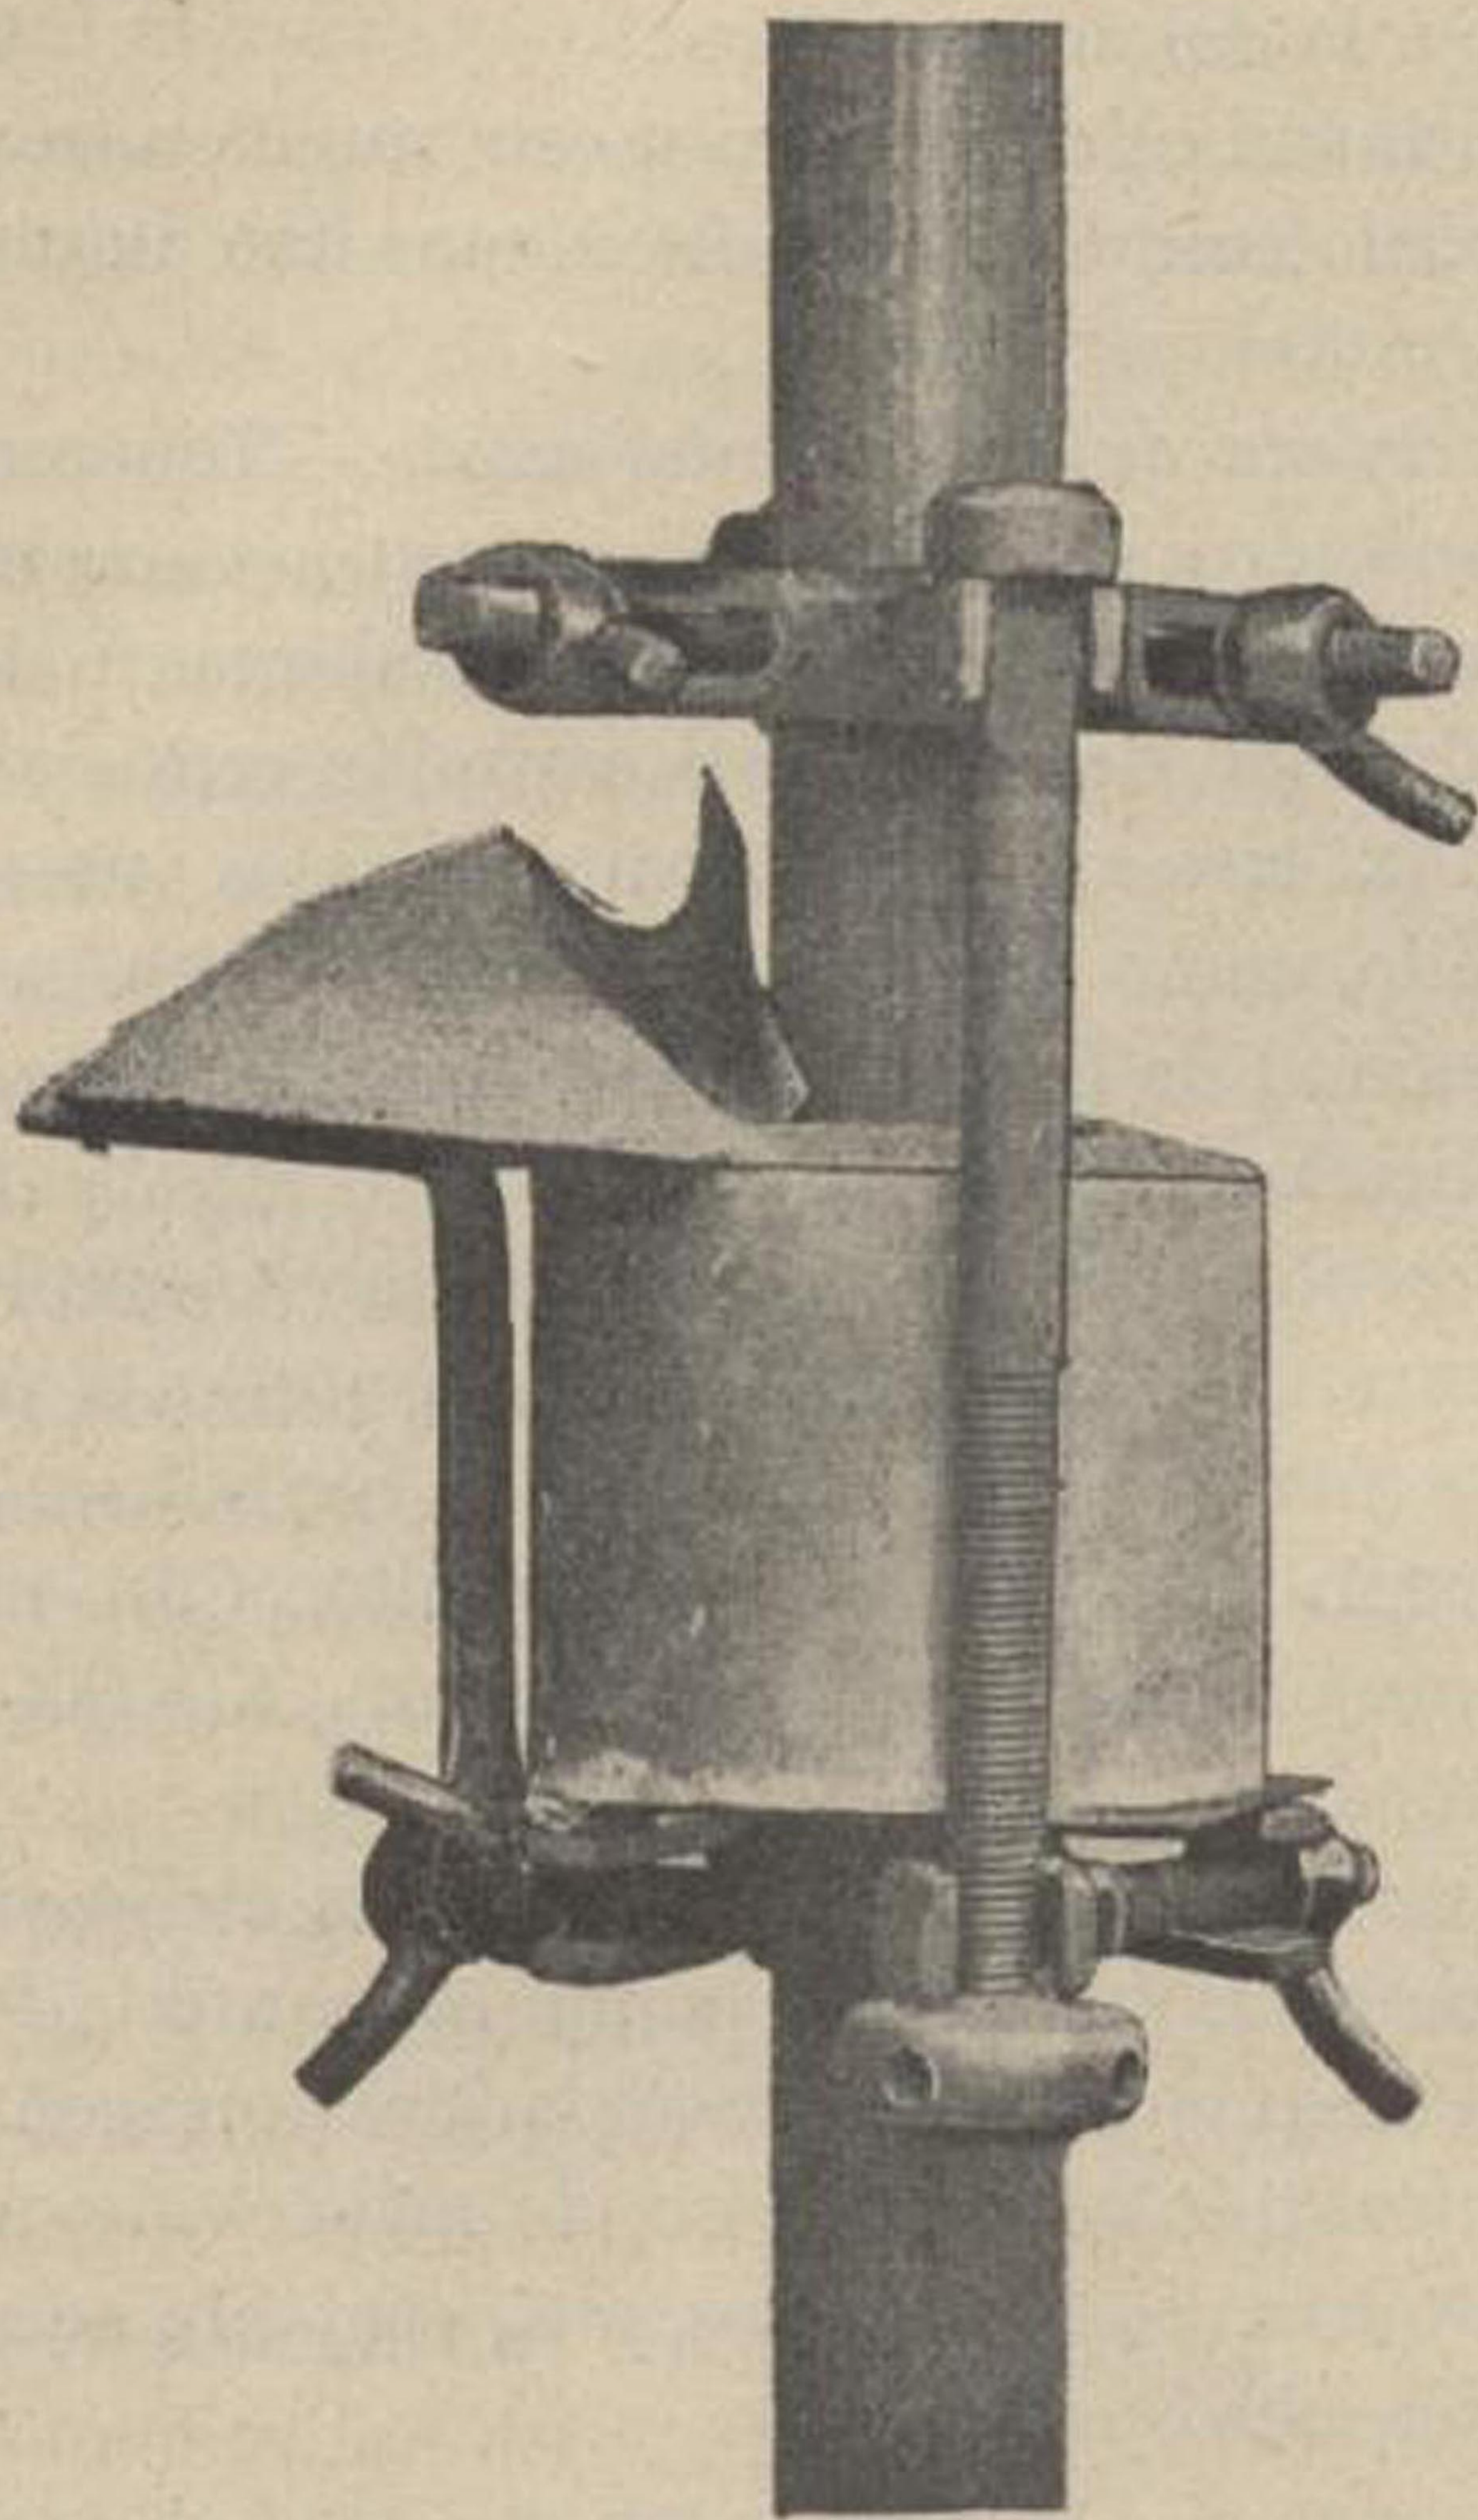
a.—Tubos verticales preparados para la soldadura.
